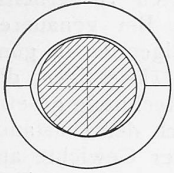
Zitronen-Spiel für künstlich gekühlte Turbomaschinenlager.
